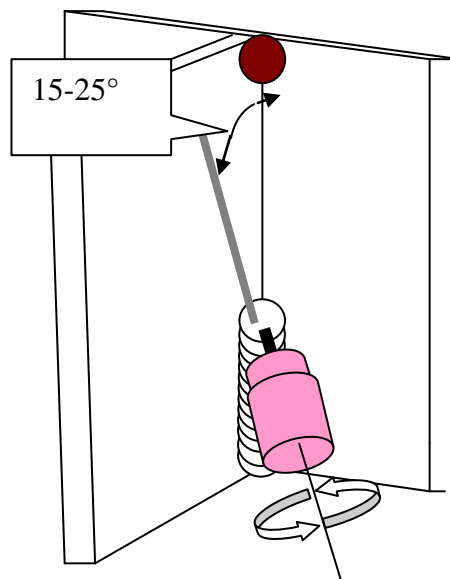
Realización de soldadura de costura de filete en posición vertical, en junta en T, sobre placas.
